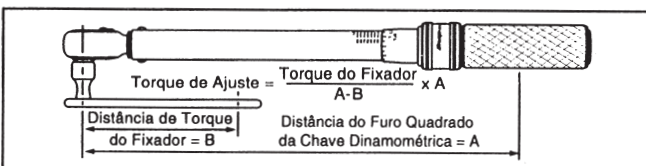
O torque do fixador é menor do que o torque do furo quadrado da chave dinamométrica.
